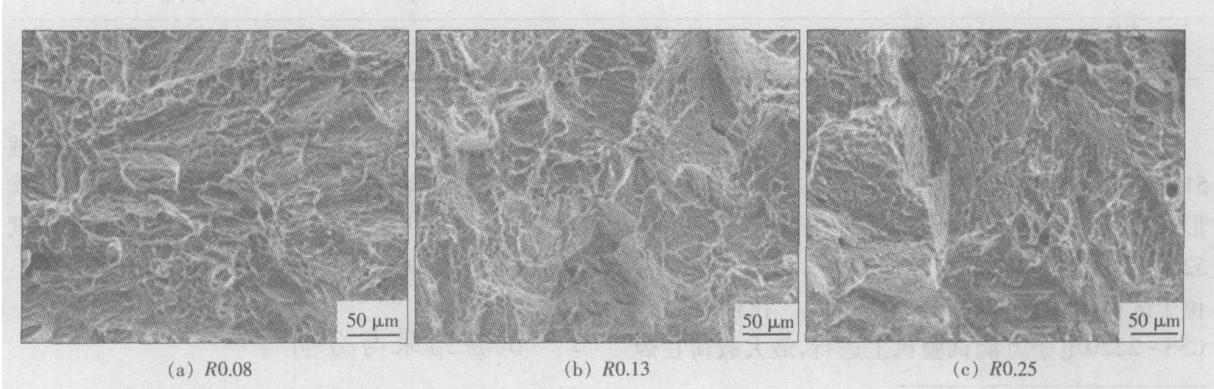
TC4 钛合金电子束焊焊缝缺口拉伸断口形貌
